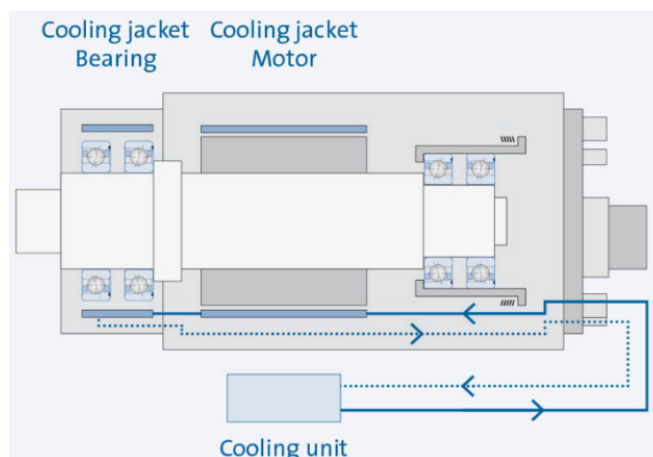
Chlazení frézovací hlavy od firmy Correa [1]
